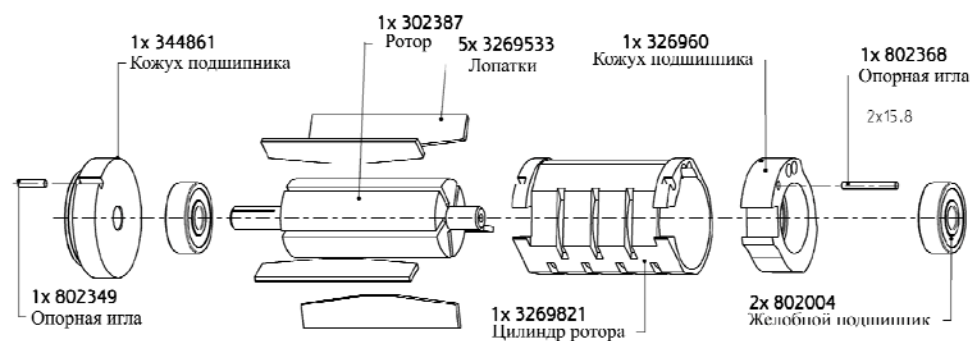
Детализовка пневматического двигателя JP-AIR 3.
